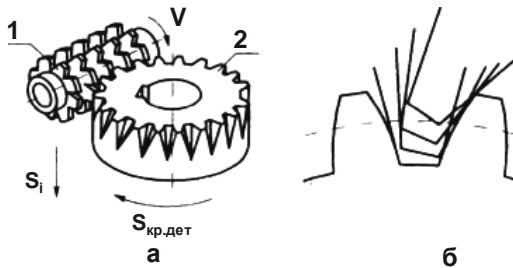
Схеми фрезерування зубів зубчастих коліс методом обкатування (обгинання): а – початкова стадія зубофрезерування:
